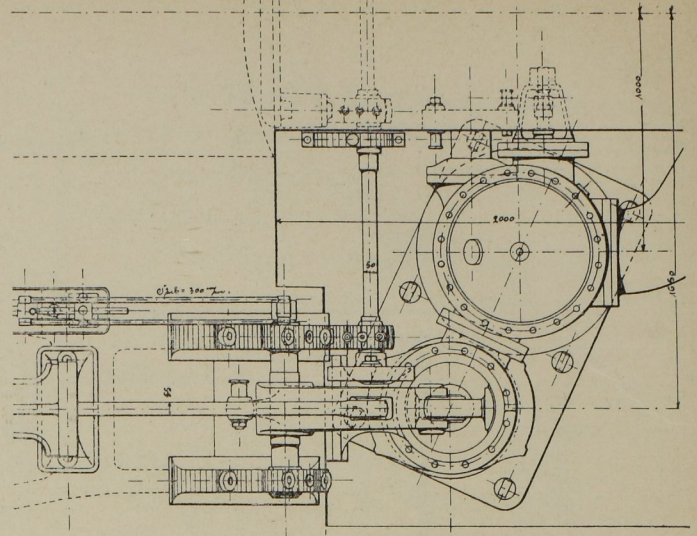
Grundriss der Pumpe mit Antrieb. Masst. 1 : 30.
